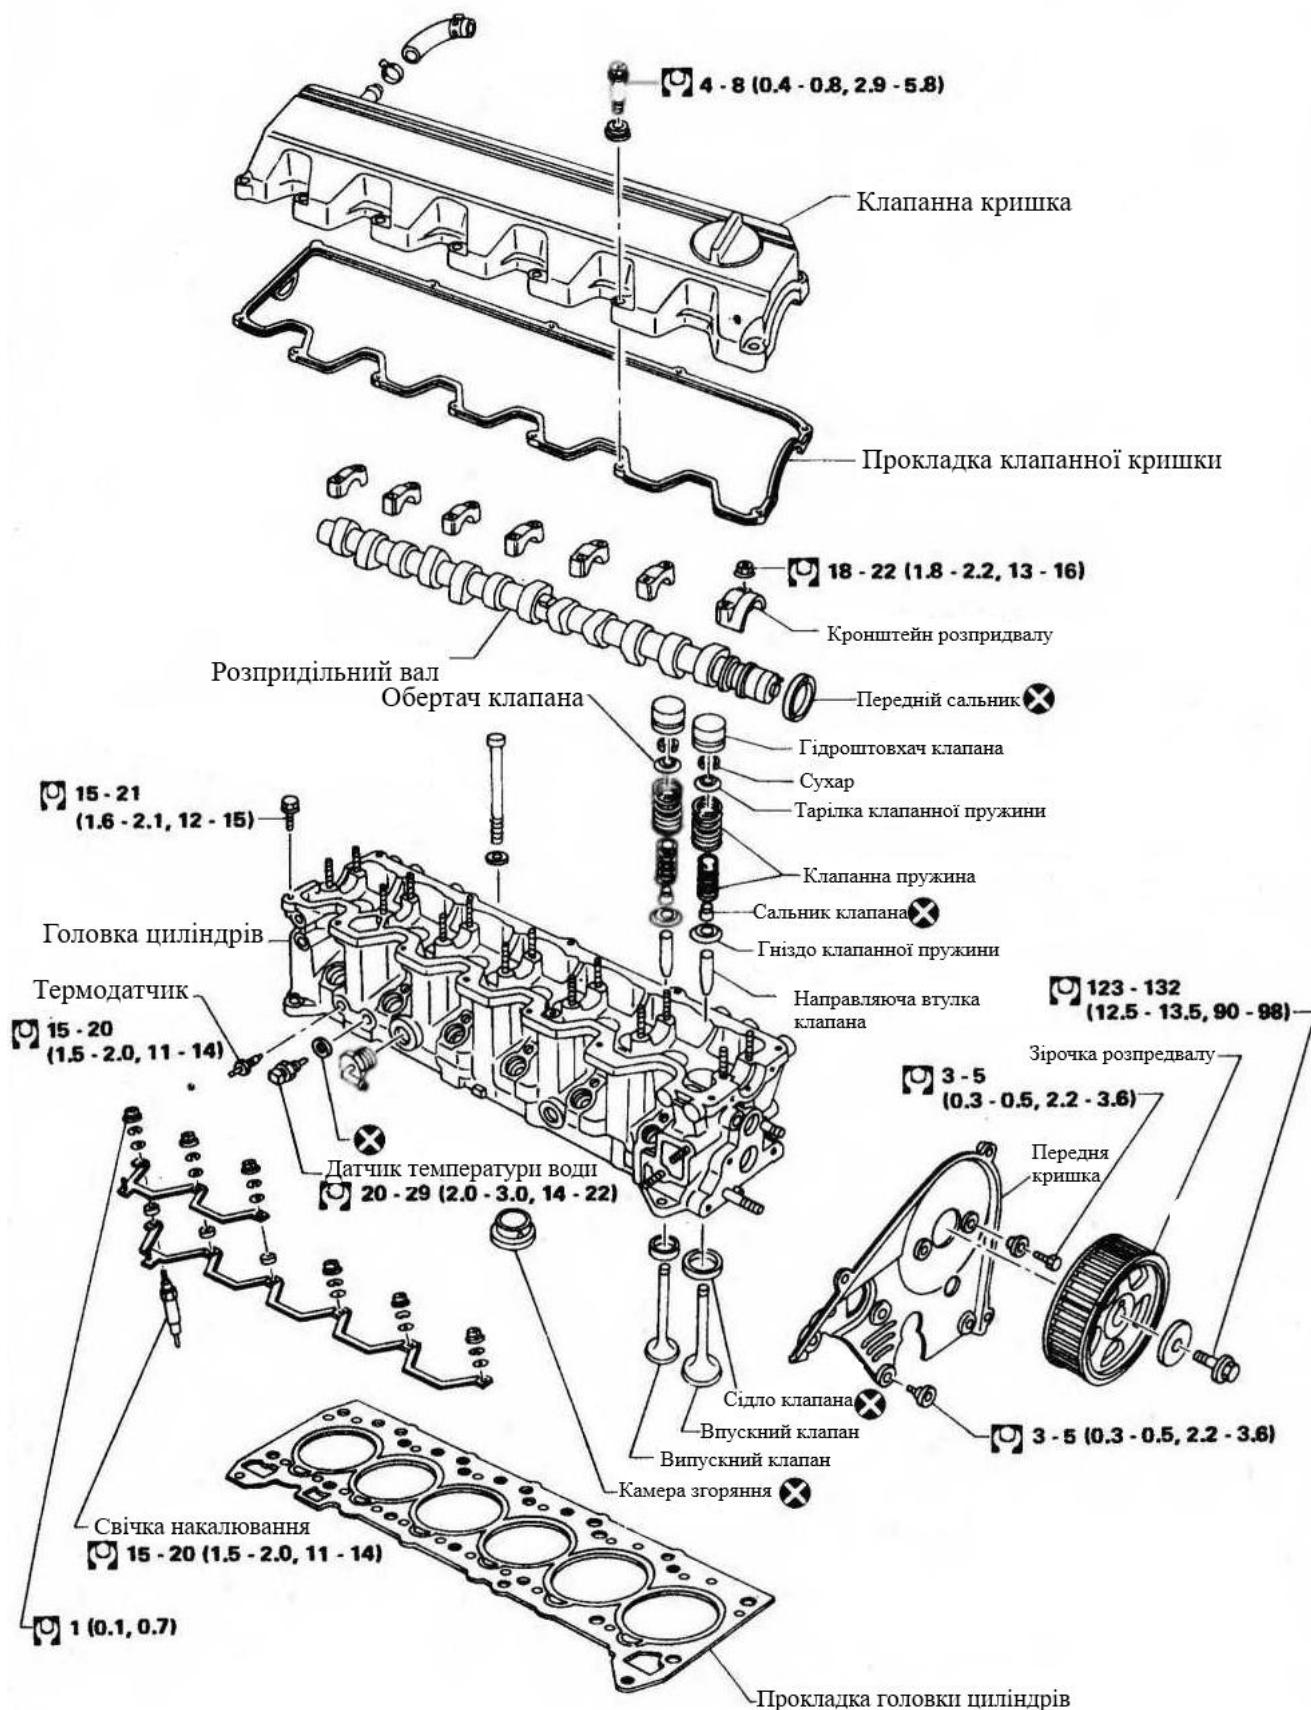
Схема розміщення складових головки циліндрів
